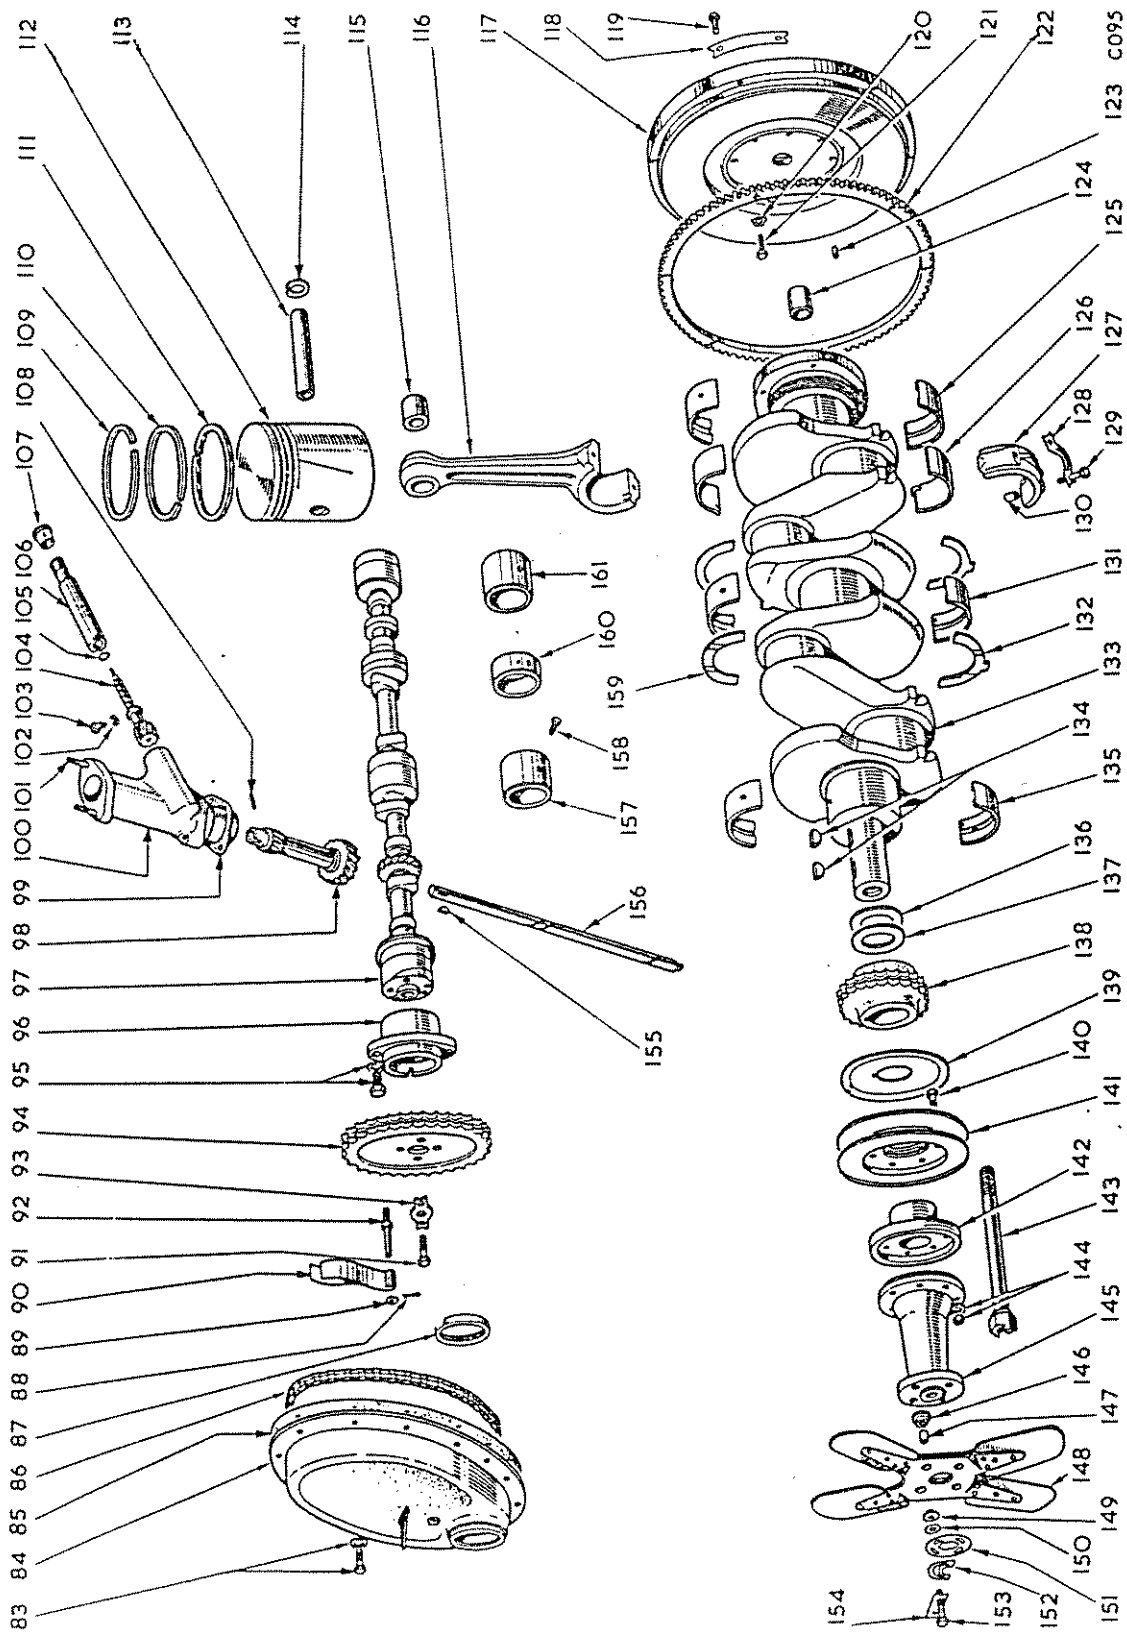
Motor (Triebwerk- und Steuerungsteile)
